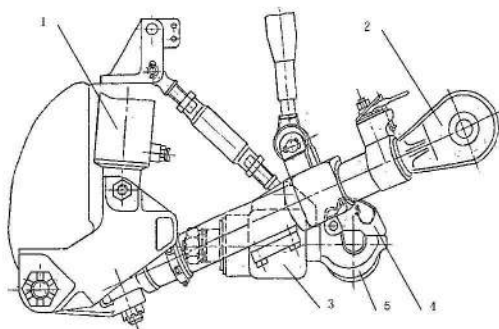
Гидрофицированный крюк: 1- цилиндр навесной системы; 2 – нижняя тяга механизма навески; 3 – корпус; 4 – собачка; 5 – буксирный крюк.
